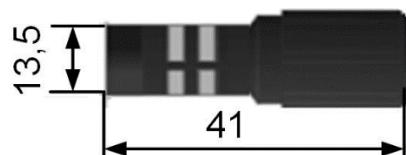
Внешний вид и габаритные размеры микрофона G14-3
